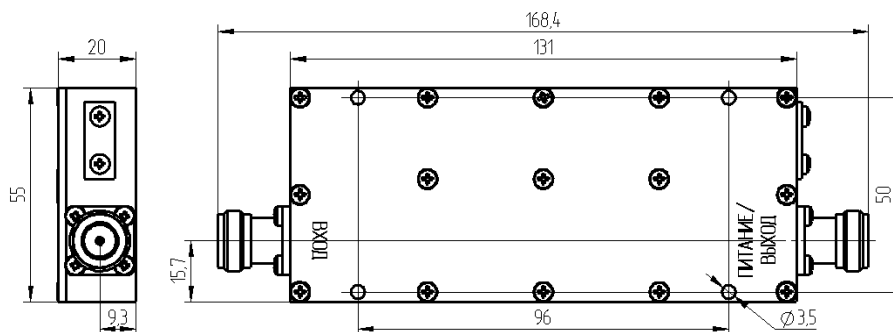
Внешний вид и габаритные размеры МШУ 1400-1700 МГц
